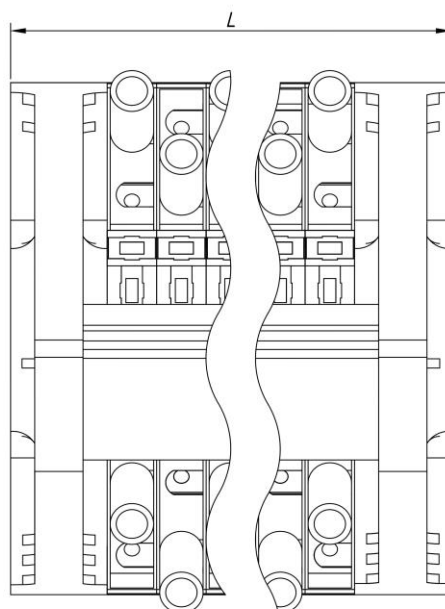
Общий вид тестовой крышки ЭПТК. Вид спереди.
